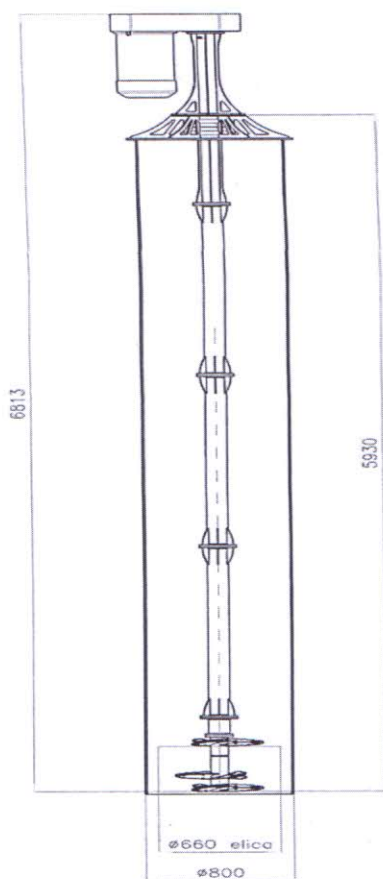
Stávající způsob separace a současný stále se ucpávající filtr.
